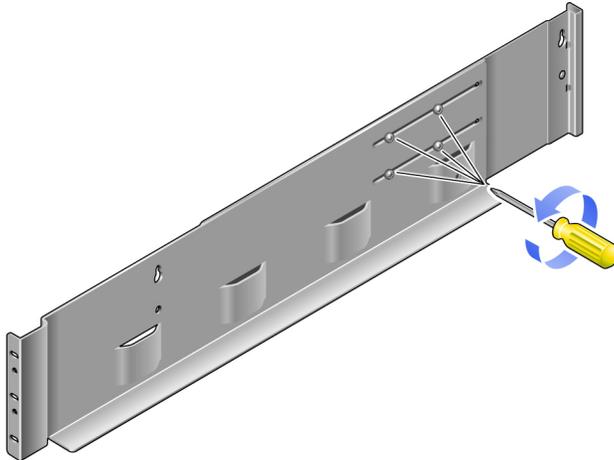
Desserrage des vis des rails pour régler la longueur des rails du plateau de contrôle
